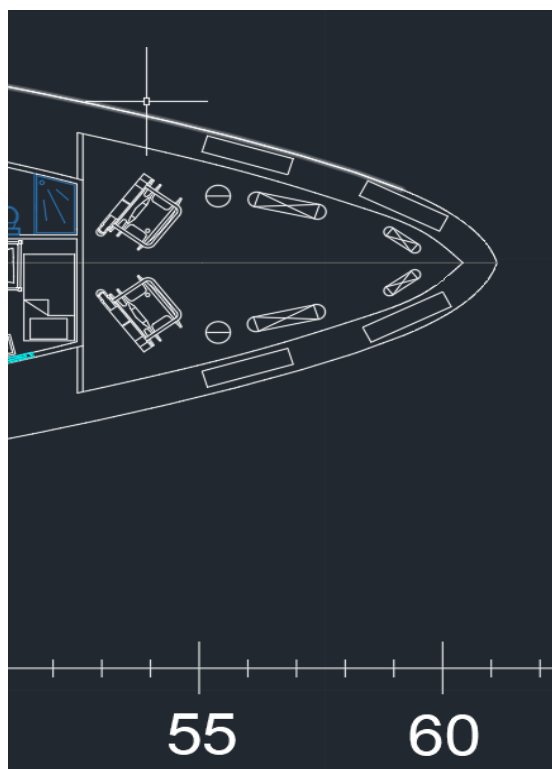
zona de amarre y fondeo en cubierta de amarre bajo el helipuerto
